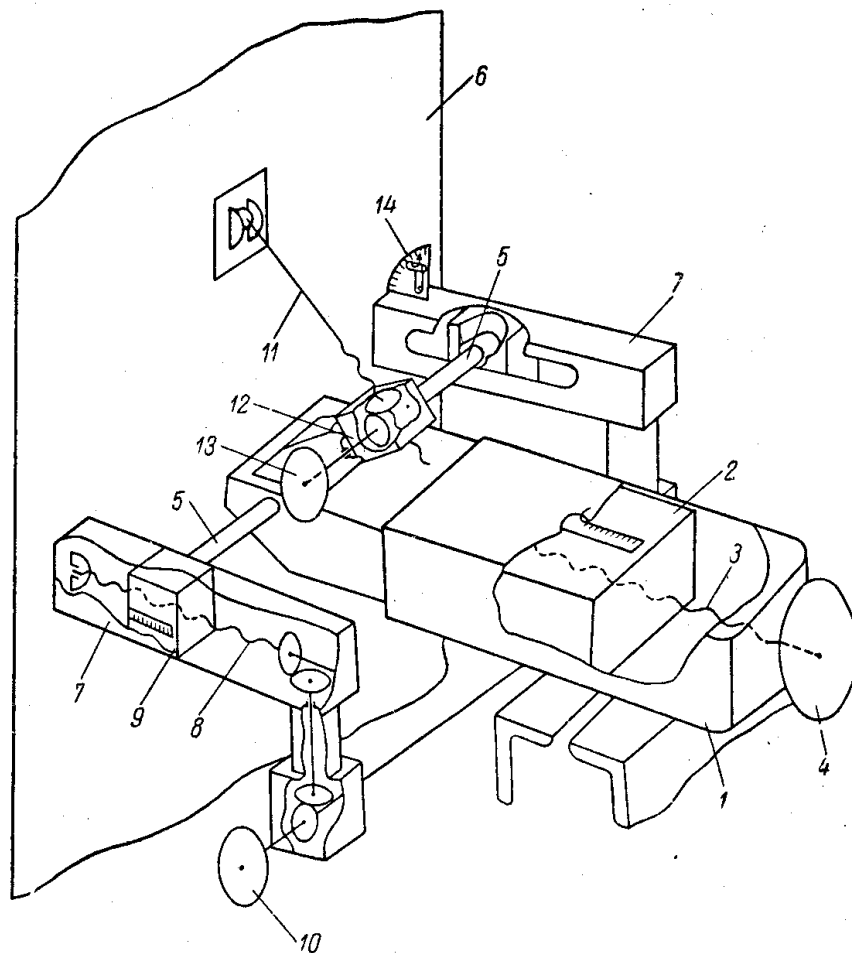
Кинематическая схема механизма установки отражающего элемента.
